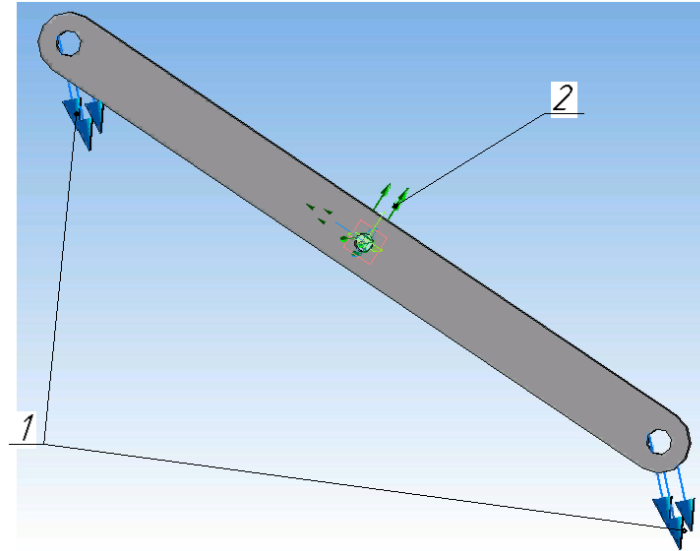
Вид трехмерной модели рычага с указанием нагрузок (1) и закреплений (2)
